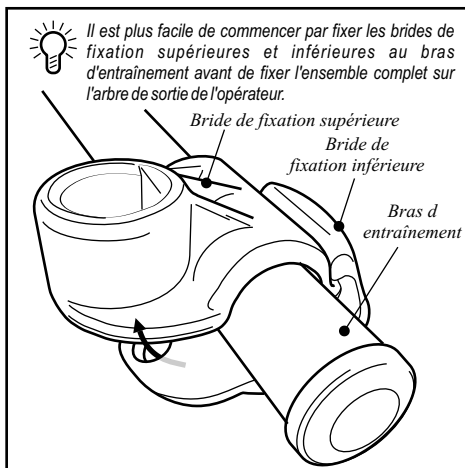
Assemblage de la bride de fixation au bras d'entraînement
